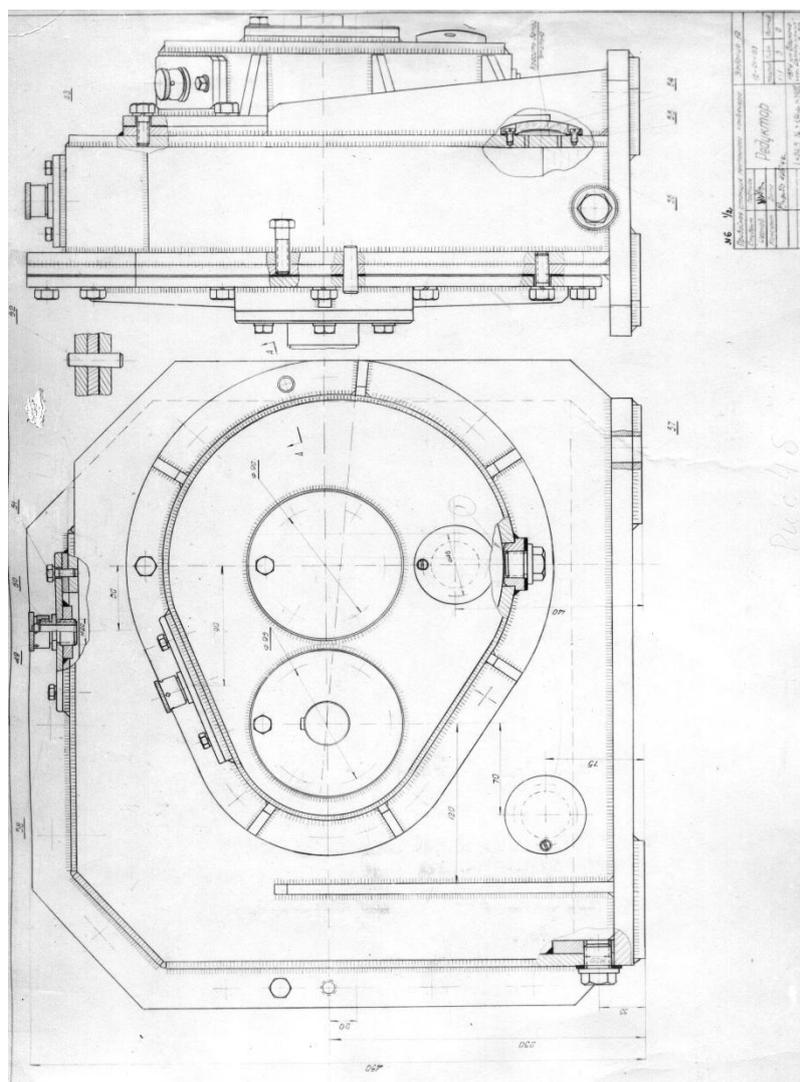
Проекция сборочного чертежа зубчатого соосного редуктора со сварным корпусом (пример)
